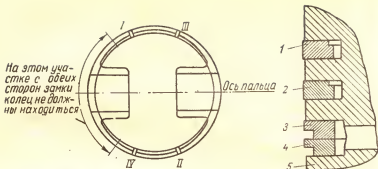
Установка поршневых колец и расположение их замков на двигателях автомобилей «Запорожец» с чугунными маслосъемными кольцами: 1 — верхнее компрессионное кольцо (хромированное, кромки тупые); 2 — нижнее компрессионное кольцо (луженое, кромки острые); 3, 4 — маслосъемные кольца; 5 — поршень. Римскими цифрами указано расположение стыков соответствующих колец.
